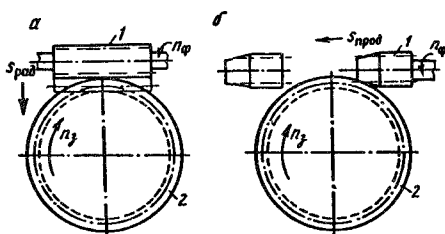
Схемы обработки зубьев червячных зубчатых колес модульной червячной фрезой
